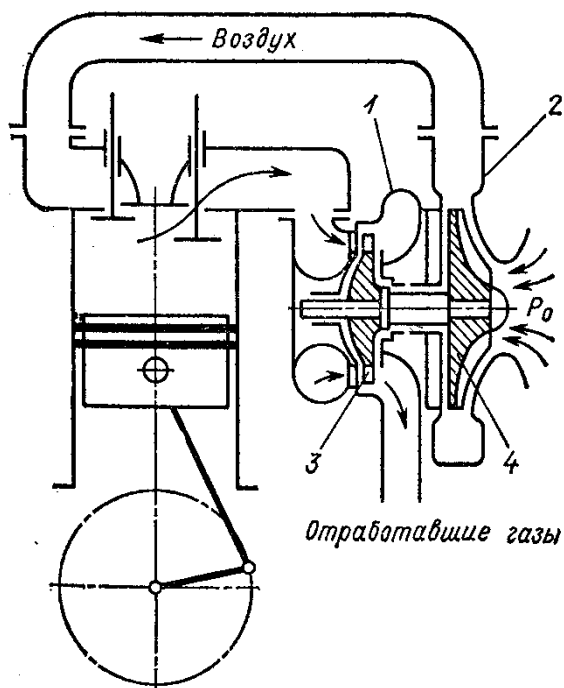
Схема газотурбинного наддува: 1 – газовая турбина; 2 – центробежный компрессор; 3 – ротор турбины; 4 – ротор компрессора
